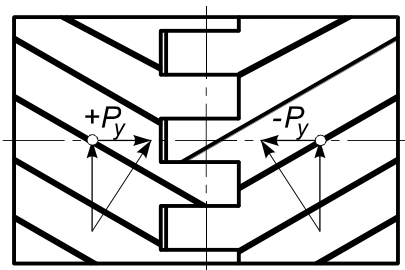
Набор фрез с различным направлением винтовой канавки (шеvronная фреза)
